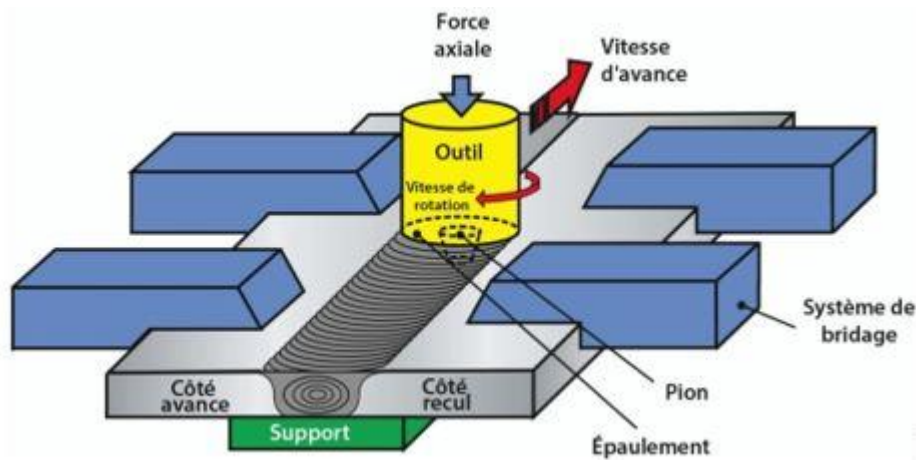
1 Illustration du procédé de soudage par friction malaxage bout à bout [1]
